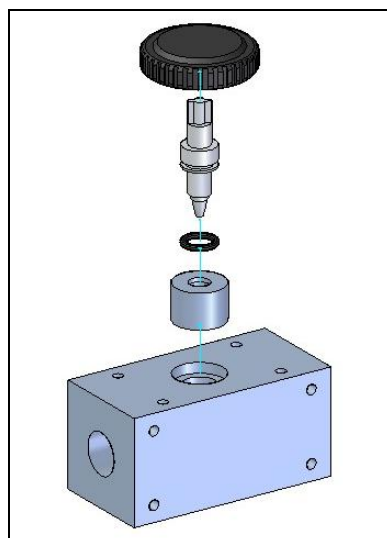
60 - Modelo de Válvula reguladora de caudal – Explosionado
